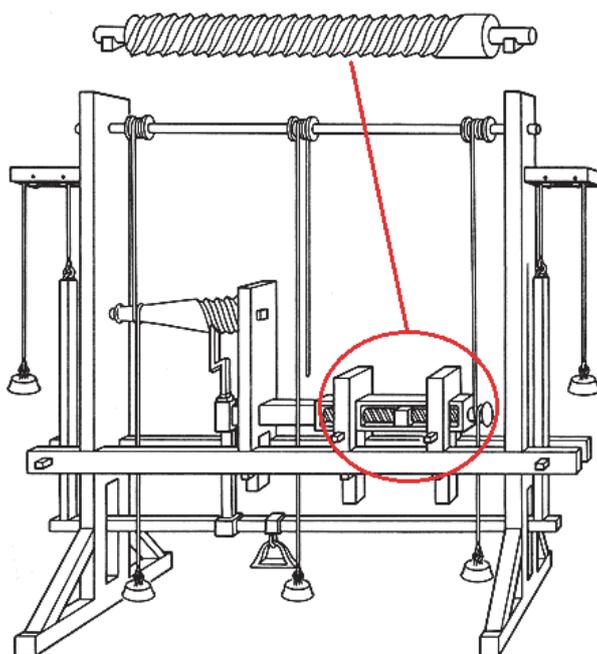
Токарно-винторезный станок. Около 1568 г. по Жаку Бессону
